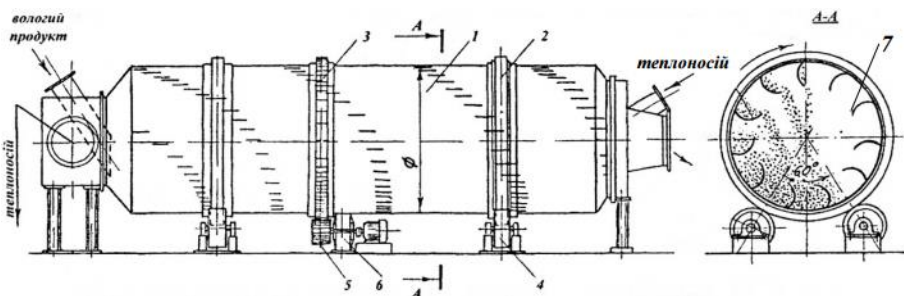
Барабанна сушарка: 1 - барабан; 2 - бандаж; 3 - зубчастий вінець; 4 - ролик; 5 - шестерня; 6 - привод; 7 – насадка
